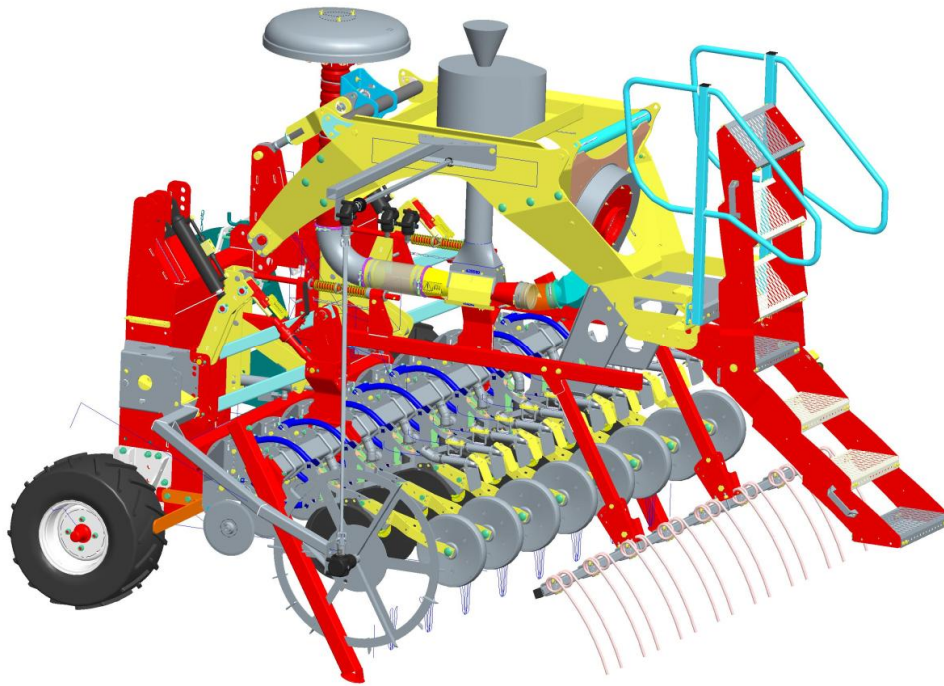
CAD-Ansicht der weitestgehend finalen Maschinenkonfiguration
